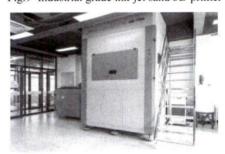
工业级激光烧结 3D 打印机 Fig.10 Industrial grade laser sintering powder 3D printer
